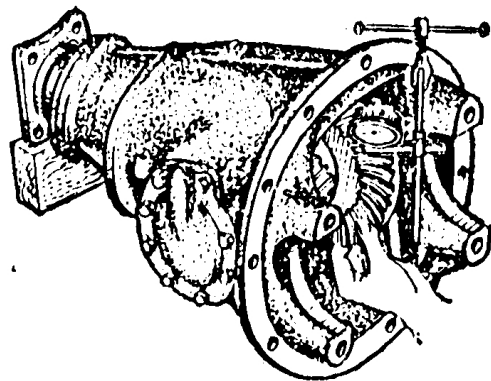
Проверка бокового зазора в зацеплении зубьев конических шестерен редуктора заднего моста автомобиля ЗИЛ-130
